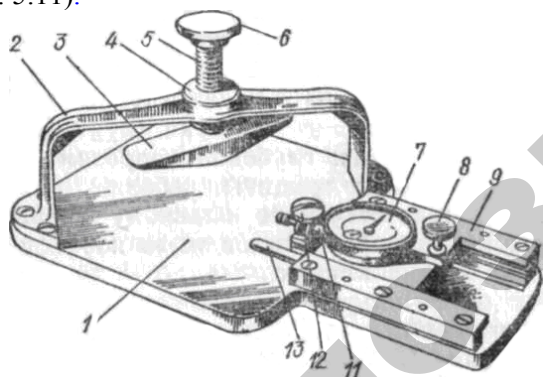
Прибор КИ-1223 для измерения радиального зазора в подшипниках качения:
